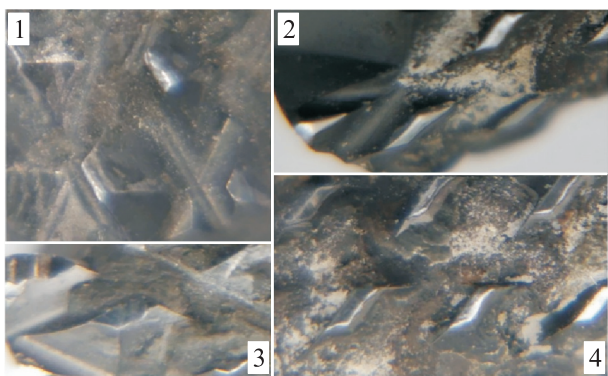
Внешний вид изношенных режущих кромок концевых фрез SECO
